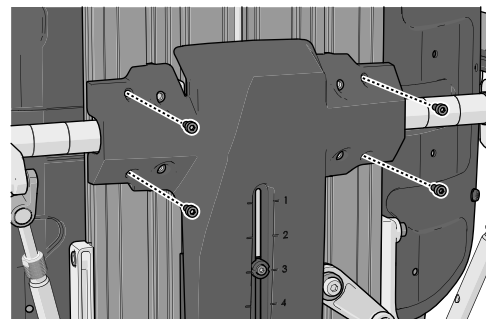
Die Anbringensorte der vier Schrauben, die die Kunststoffabdeckung sichern.
